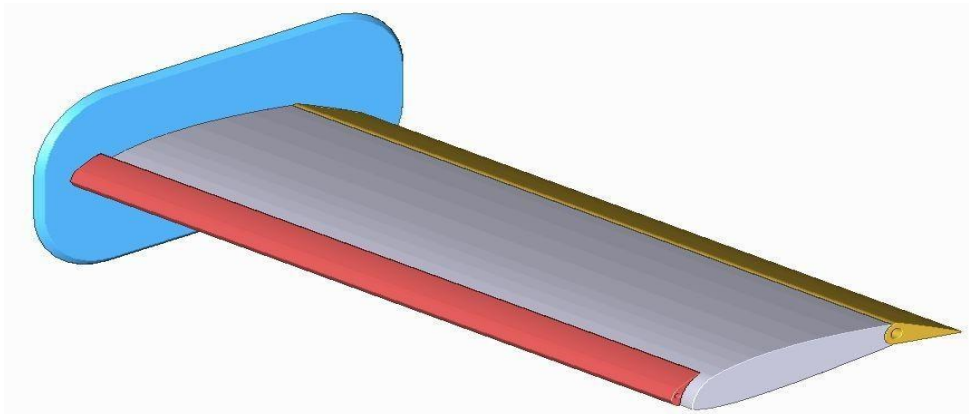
Desenho em CAD apresentando o conjunto que será construído.
